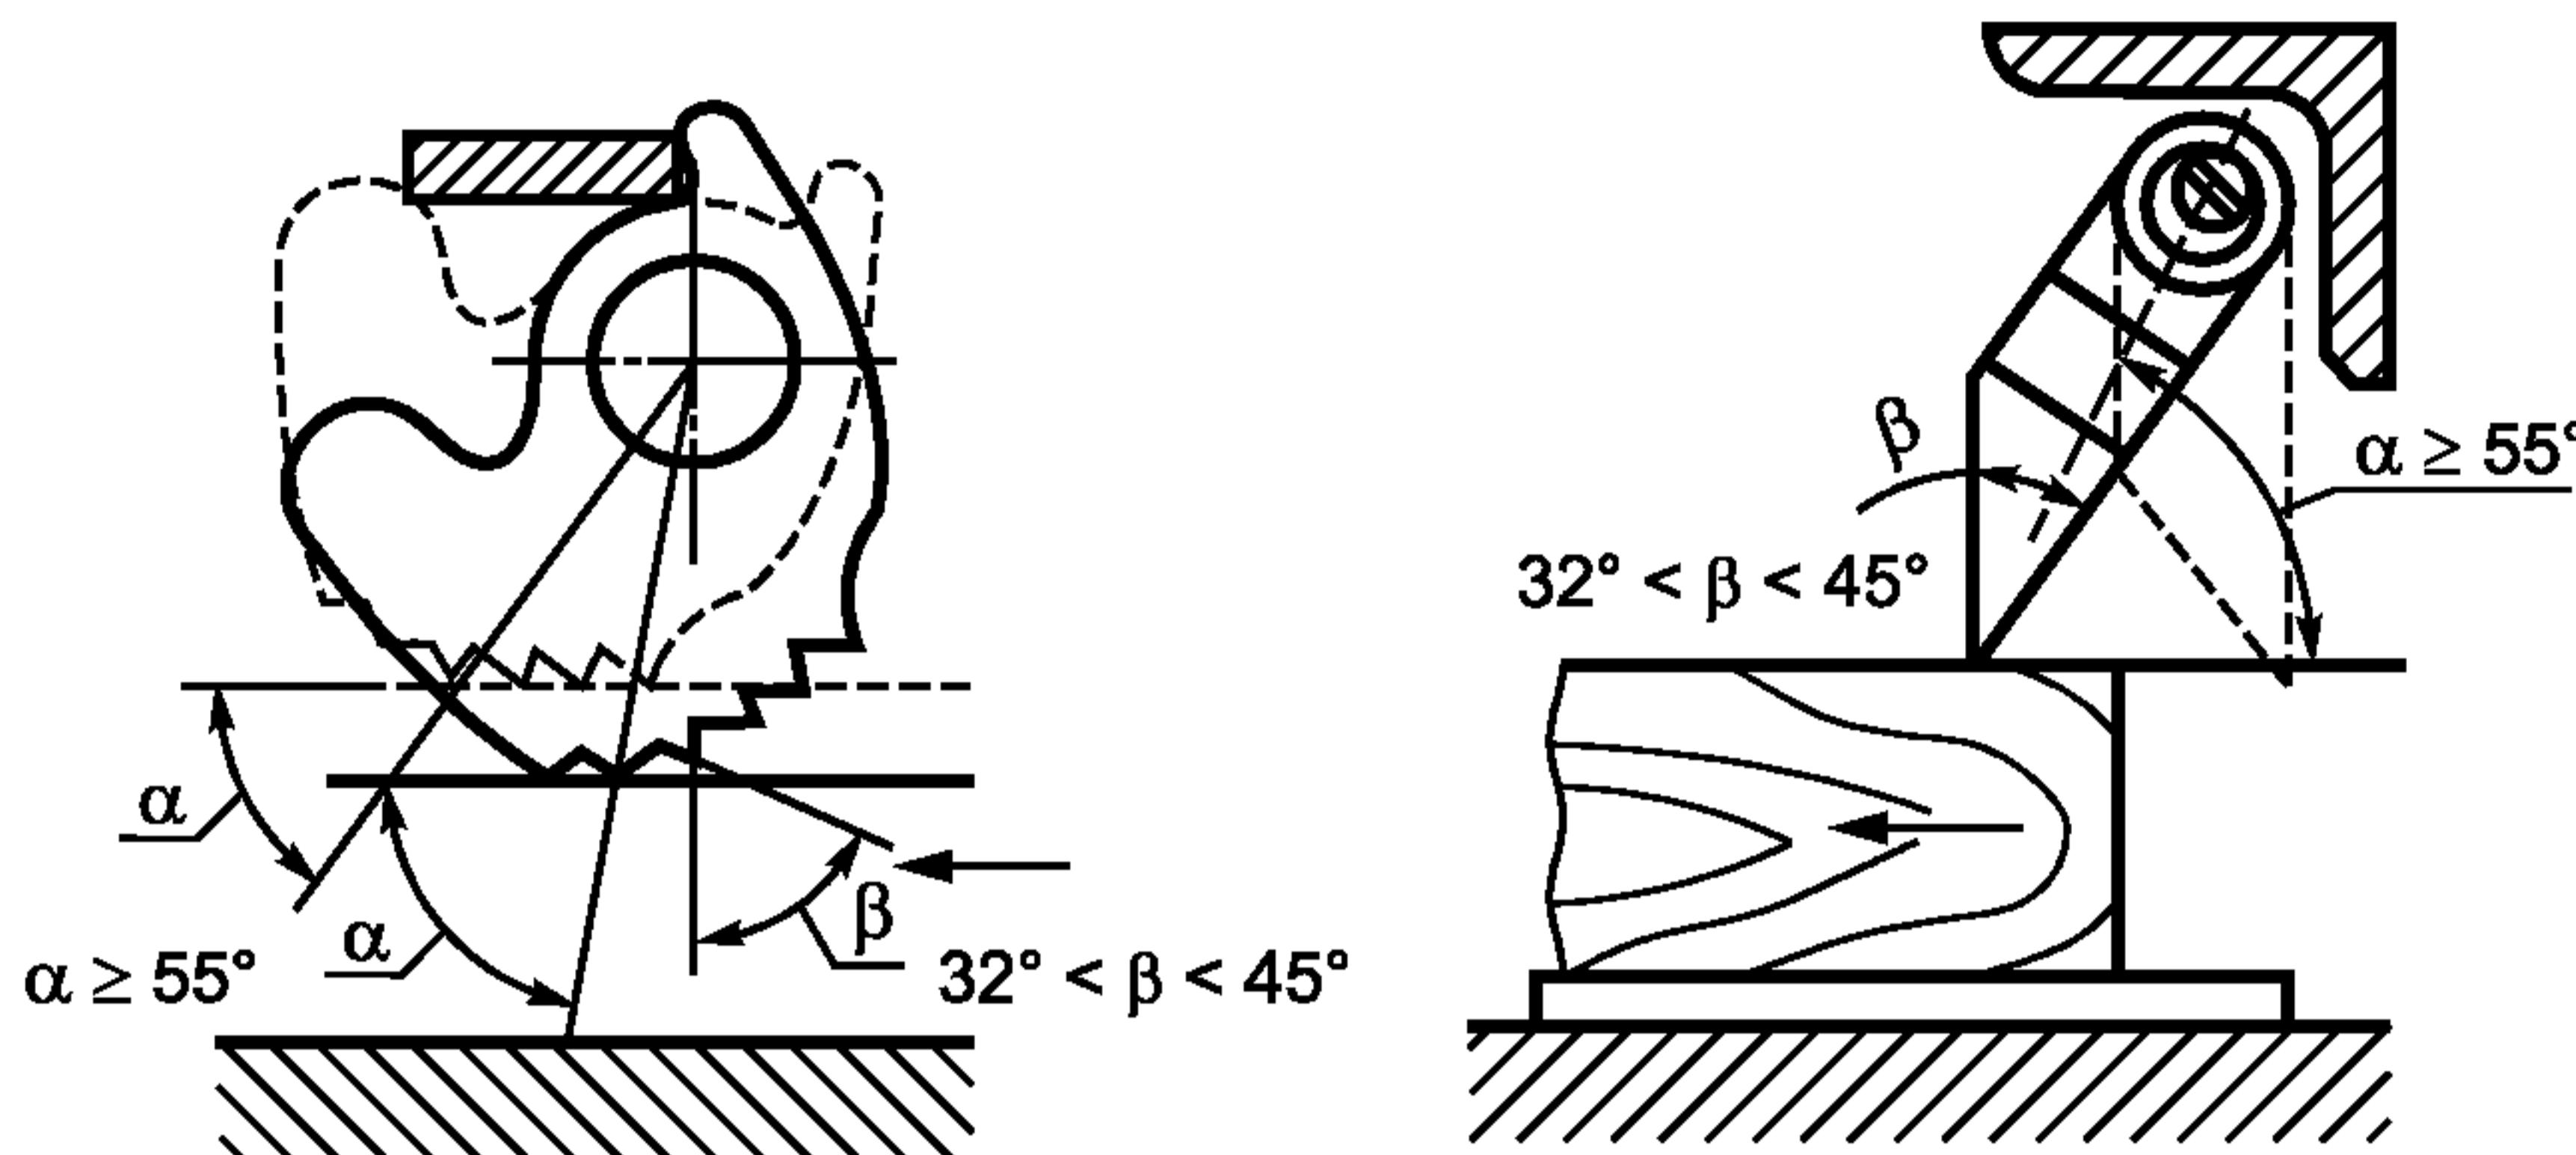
Пример устройства противовыбрасывающего устройства с качающимися элементами (стрелка указывает направление подачи)
